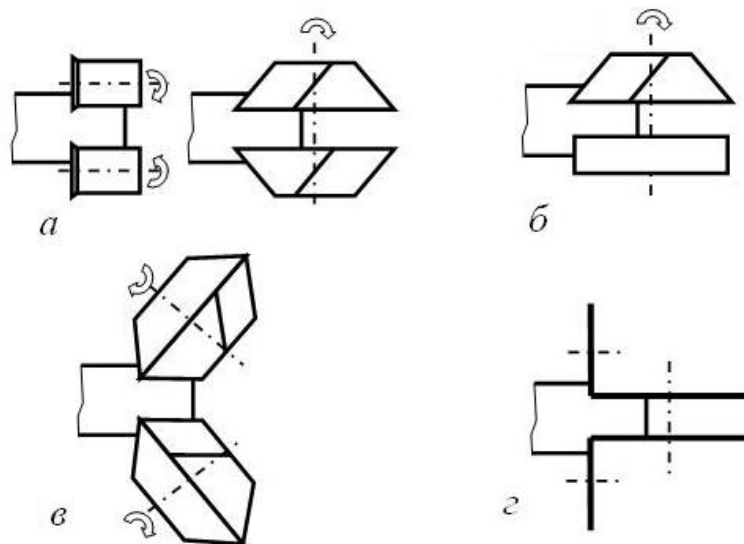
Варианты выполнения операции нарезания прямых рамных шипов: *а* – цилиндрическими фрезами с последующей подсечкой плечиков; *б* – торцово-коническими фрезами; *в* – коническими фрезами; *г* – пилами
